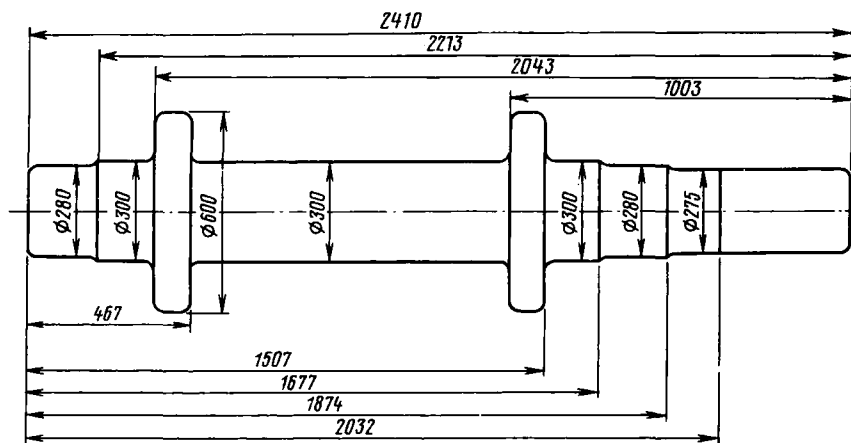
Главный приводной вал эскалатора ЭМ-4
